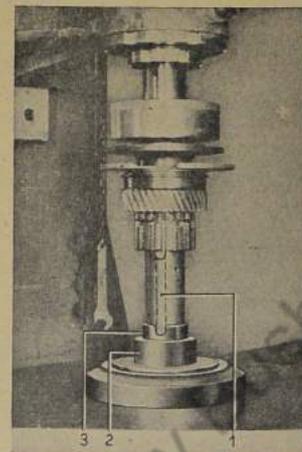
Laufbuchse zum Schrägrad für 3. Gang aufpressen
